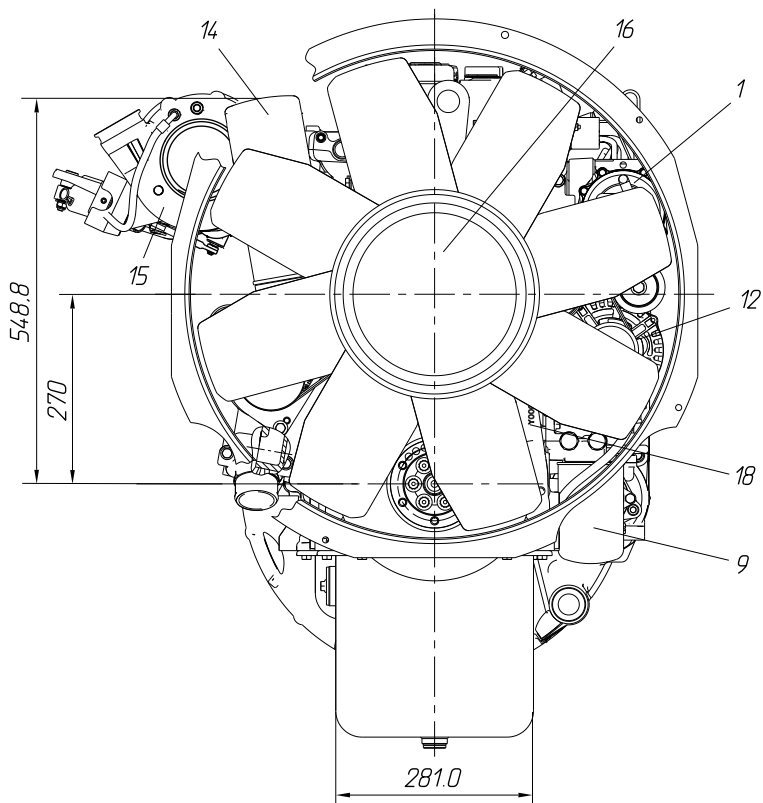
Габаритные размеры, расположение агрегатов и узлов двигателя ЯМЗ-Э5367 (вид спереди):
